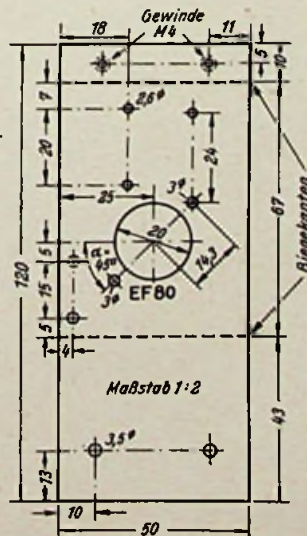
Maßskizze für das Chassis aus 2 mm starkem Aluminiumblech
